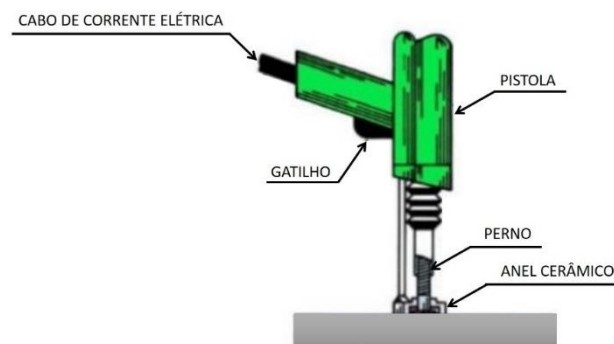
Esquema de soldadura de pernos (adaptado de [67])
